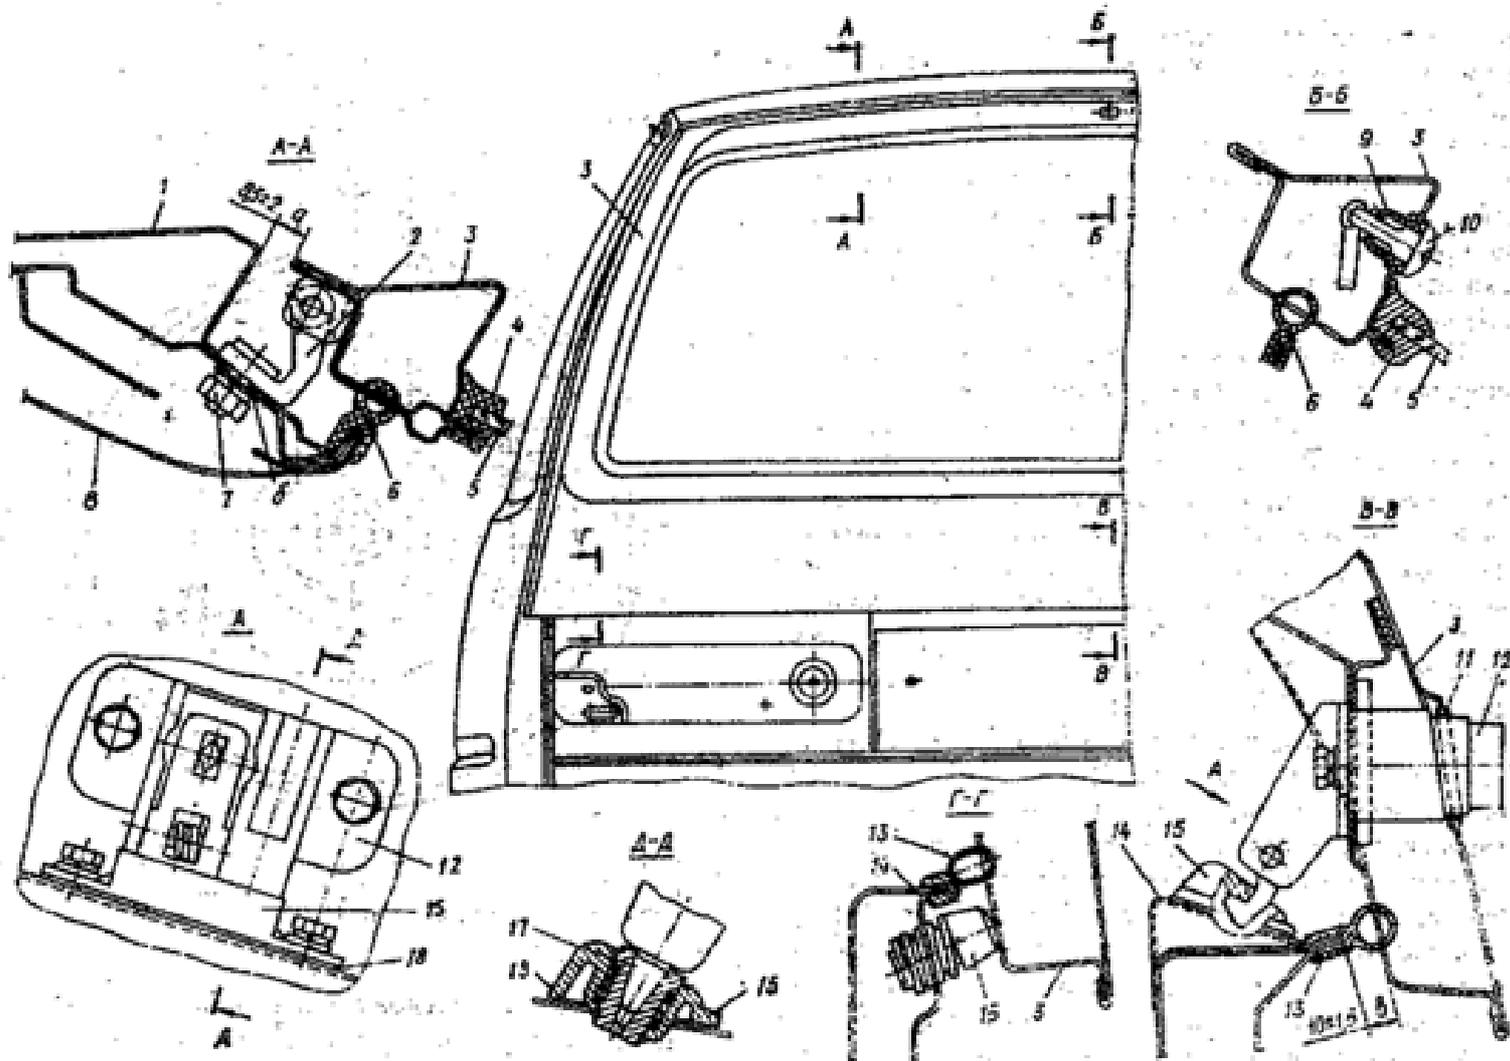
Арму́ра двери задка трехдверного автомобиля: 1 - кузов; 2 - петля; 3 - дверь задка; 4 - уплотнитель стекла; 5 - стекло двери задка; 6 - уплотнитель боковой; 7 - гайка крепления петли; 8 - заглушка; 9 - уплотнитель жиклера; 10 - жиклер стеклоомывателя; 11 - прокладка замка; 12 - замок двери задка; 13 - уплотнитель нижний; 14 - панель задка кузова; 15 - фиксатор двери задка; 16 - ограничитель двери; 17 - шип замка; 18 - прокладка регулировочная; а - зазор между дверью и крышей; б - увеличенные отверстия на кузове для крепления петли; в - зазор между дверью и торцами панели задка.
